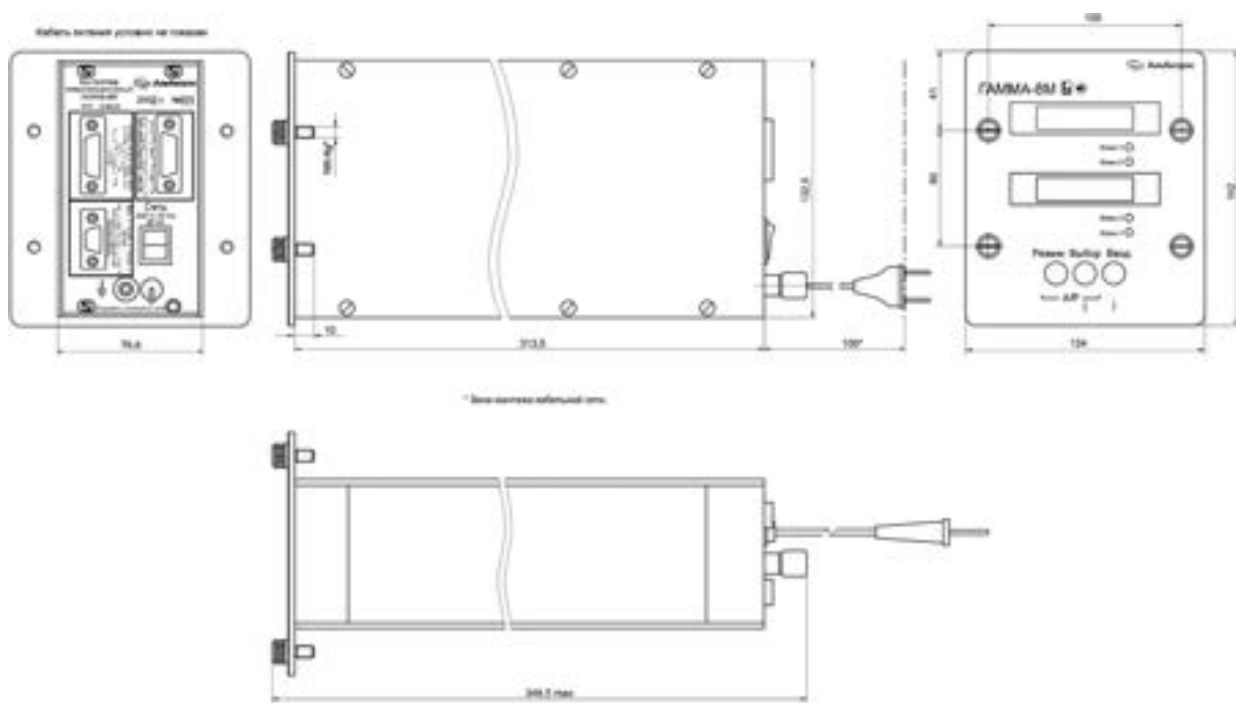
Внешний вид и габаритные размеры прибора
